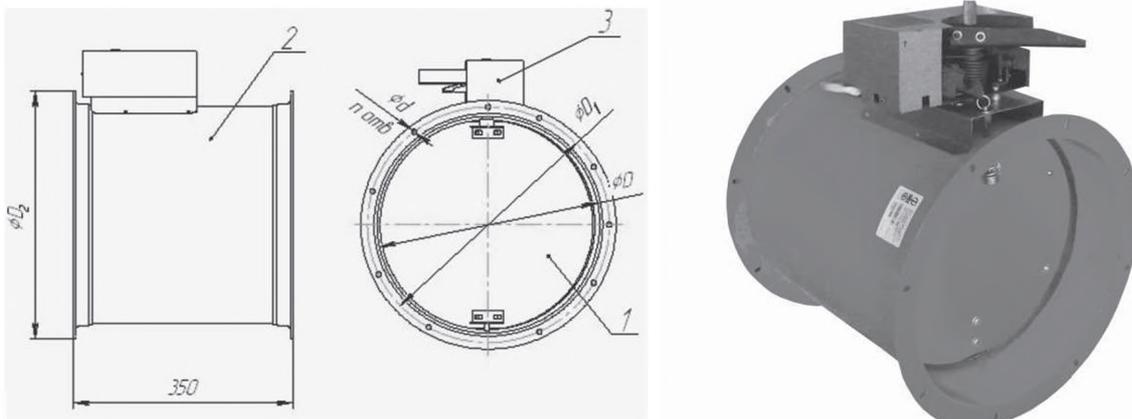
Клапан противопожарный (огнезадерживающий) фланцевый с электромагнитным приводом.
